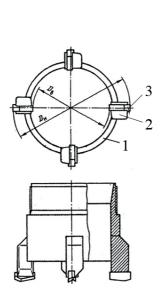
Твердосплавная коронка типа М6: 1 – корпус; 2 – ребра; 3 – твердосплавные пластины; $D_{\scriptscriptstyle \rm H}$ – наружный диаметр; $D_{\scriptscriptstyle \rm B}$ – внутренний диаметр
